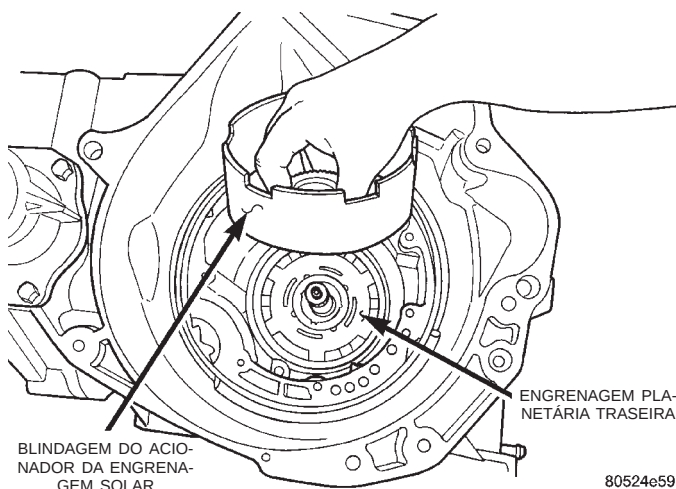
Blindagem do Acionador da Engrenagem Solar
